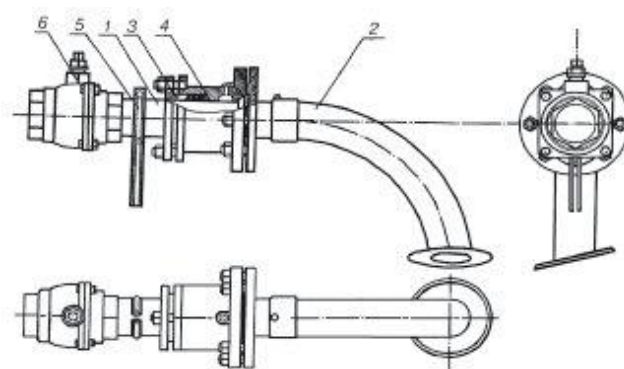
Общий вид крана сифонного КС:(1 — труба; 2 — отвод; 3 — втулка сальника; 4 — корпус; 5 — ручка; 6 — кран шаровый проходной).
